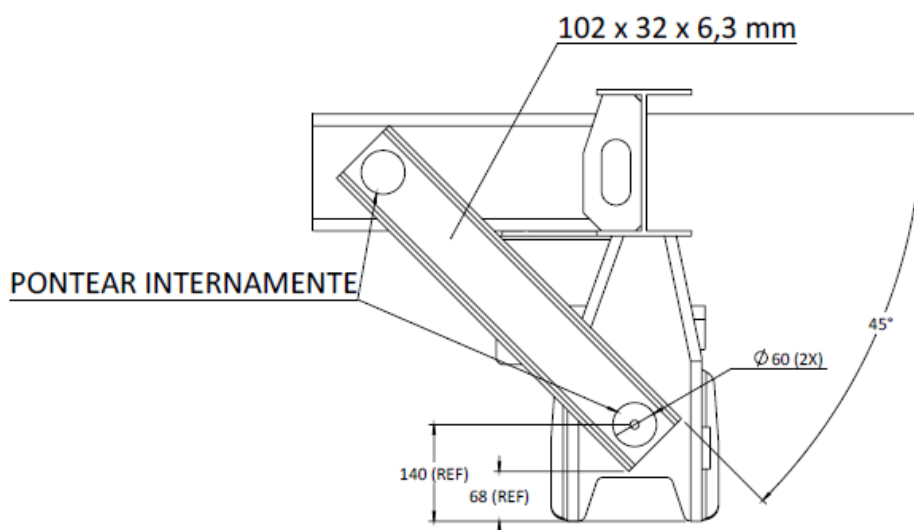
Posicionamento do reforço de ligação da travessa e suporte frontal
